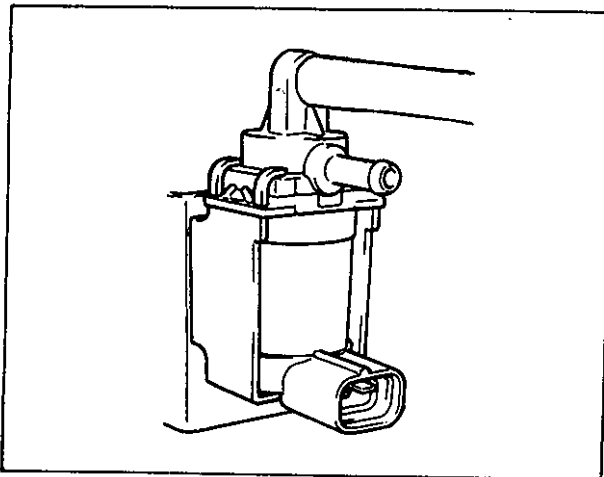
E-142 Inspección de la válvula de solenoide de ISC (1)
